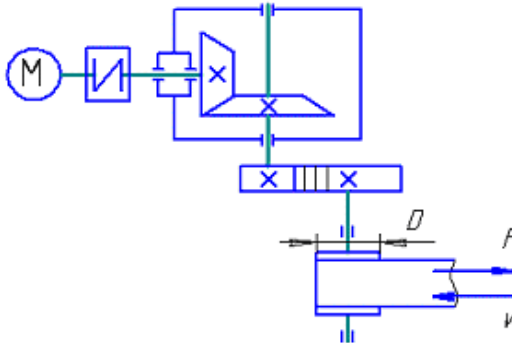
Кинематическая схема привода ленточного конвейера
